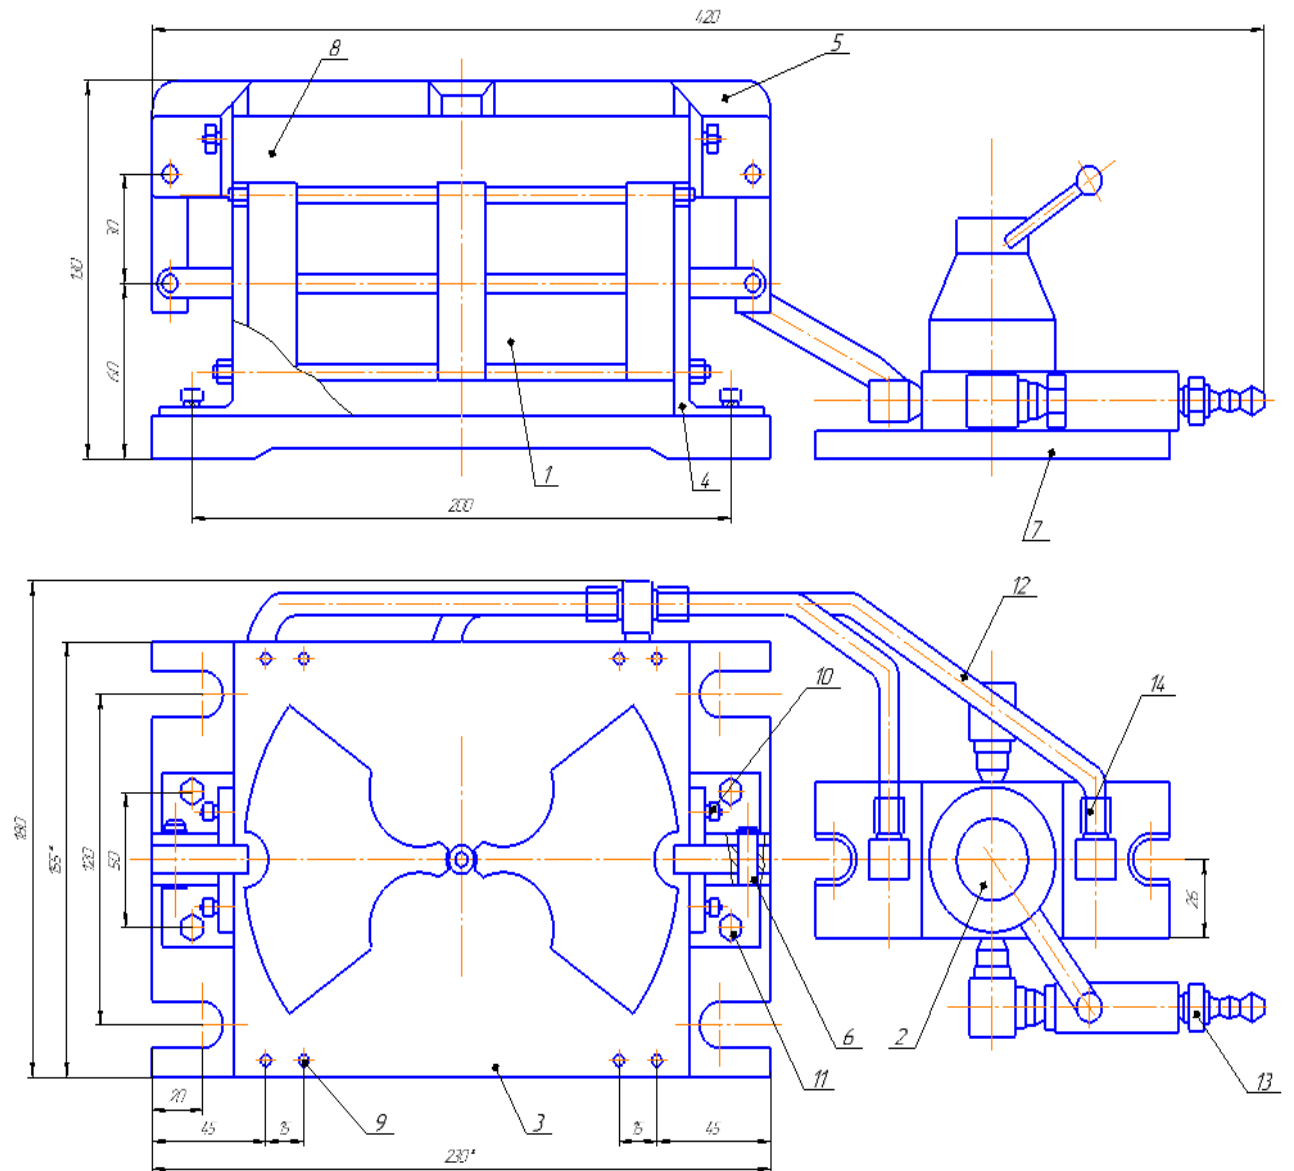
Загальний вид пневматичного пристрою для фіксації платиків при фрезеруванні: 1 – пневматичний циліндр; 2 – пневматичний кран; 3 – основа; 4 – передня стійка; 5 – прихвати; 6 – пальці; 7 – основа крана; 8 – задня стійка; 9, 10, 11 – різьбові з'єднання; 12 – металеві труби; 13 – наконечник; 14 – штуцер
